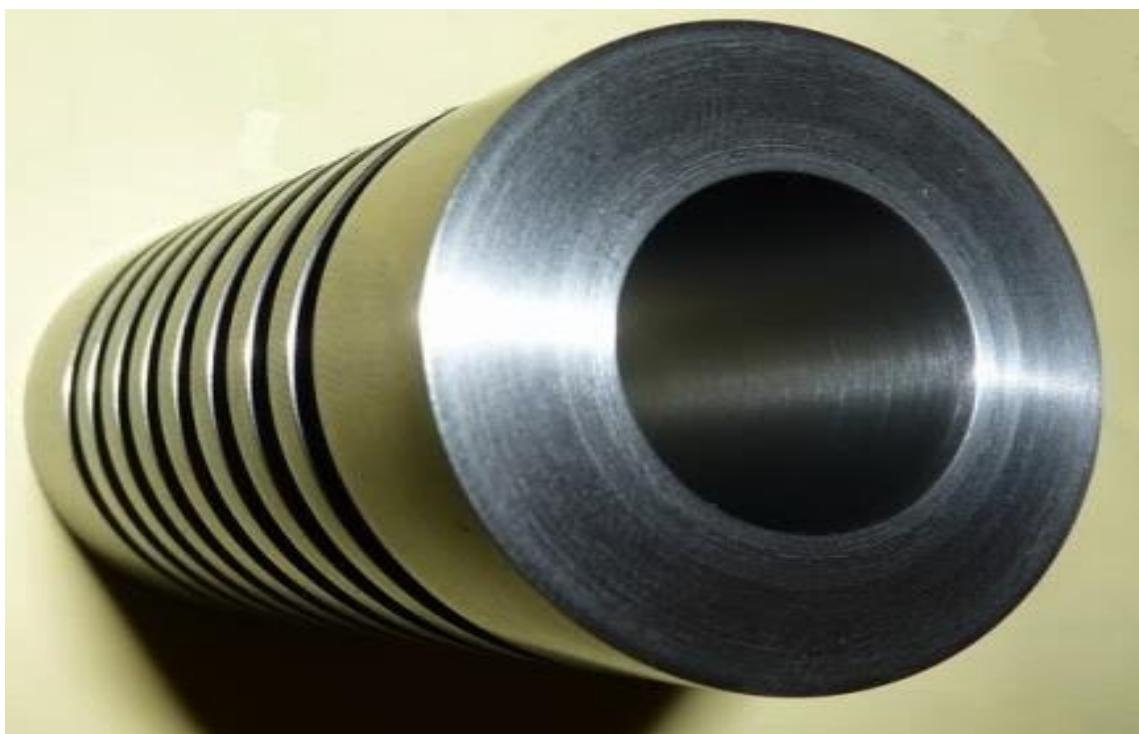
Prilikom odrezivanja lagano pridržavati cilindar
